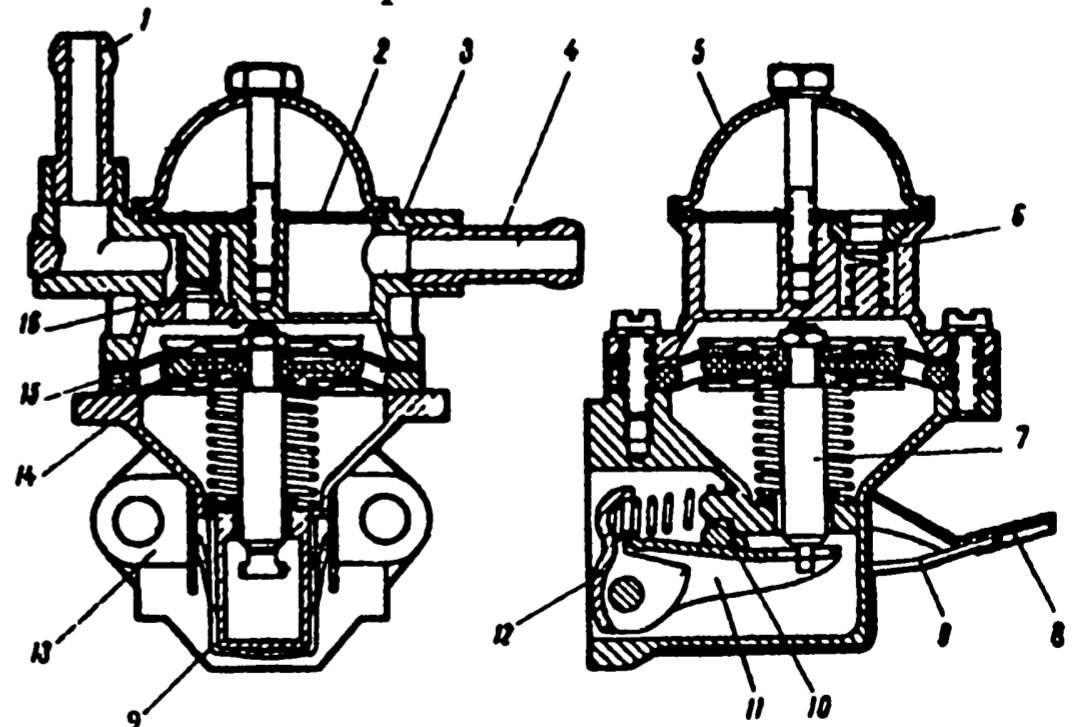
Топливный насос: 1 - нагнетательный патрубок; 2 - фильтр; 3 - корпус; 4 - всасывающий патрубок; 5 - крышка; 6 - всасывающий клапан; 7 - тяга; 8 - рычаг ручной подкачки топлива; 9 - пружина; 10 - эксцентрик; 11 - балансиры; 12 - рычаг механической подкачки топлива; 13 - нижняя крышка; 14 - внутренняя дистанционная прокладка; 15 - наружная дистанционная прокладка; 16 - нагнетательный клапан
